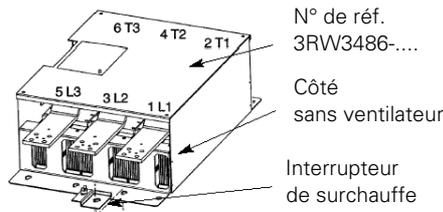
Montage de l'interrupteur de surchauffe pour 3RW34 86
